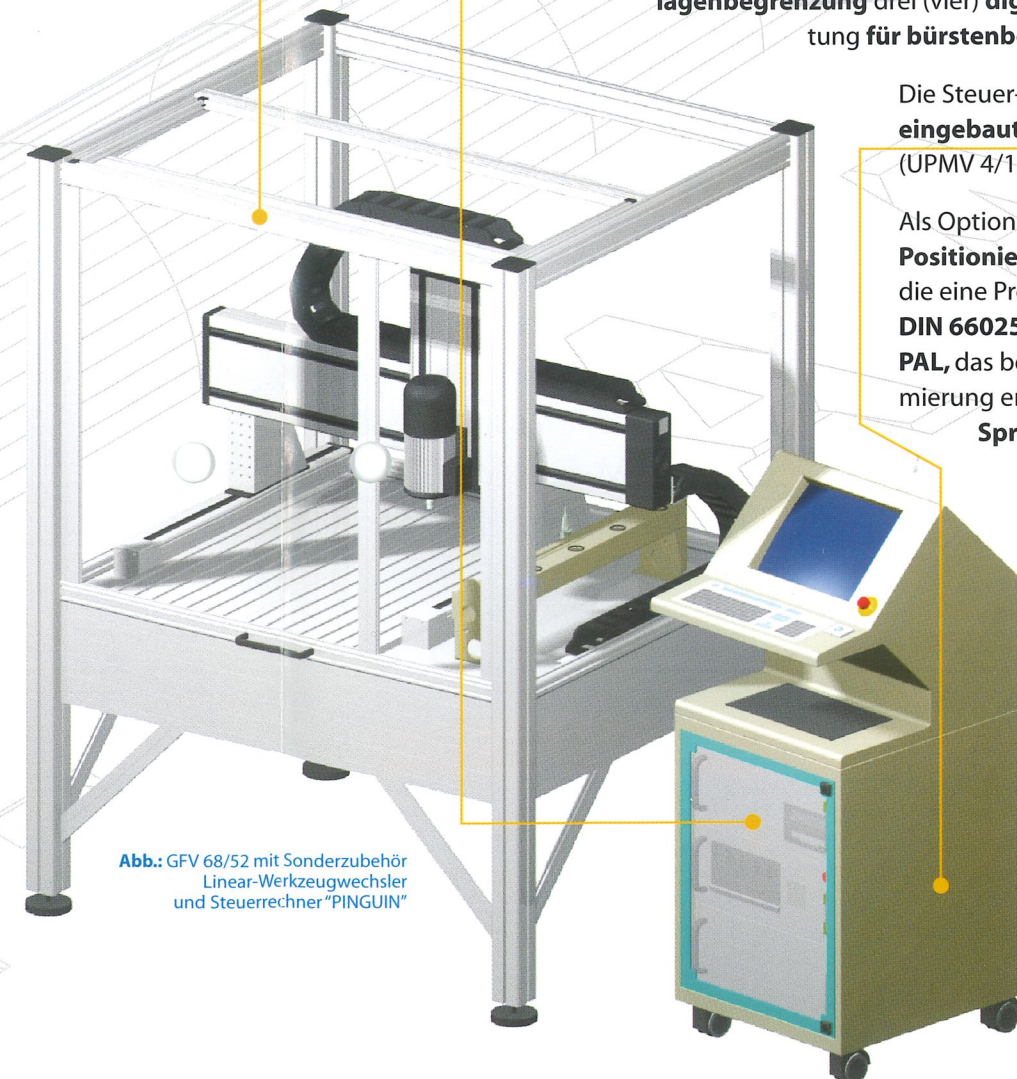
/52 mit Sonderzubehör Linear-Werkzeugwechsler und Steuerrechner "PINGUIN"
